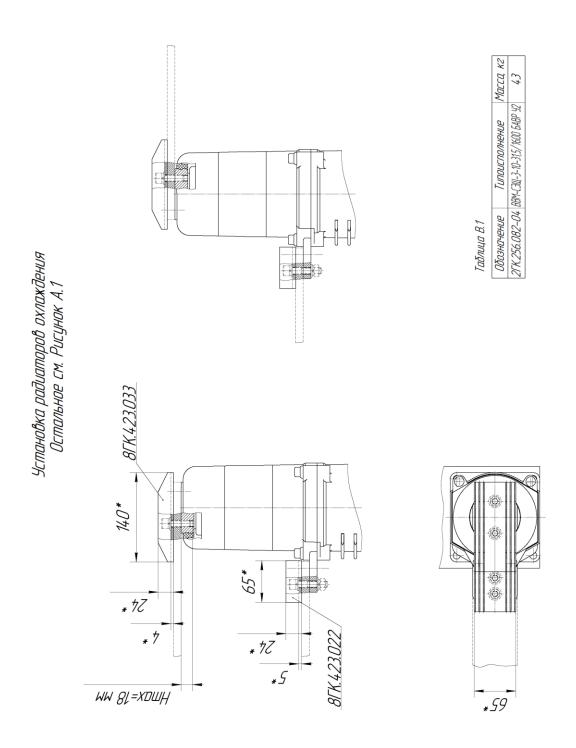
Габаритные, присоединительные и установочные размеры выключателя типа ВВМ-СЭЩ-3-10-31,5/1600 БАВР У2
